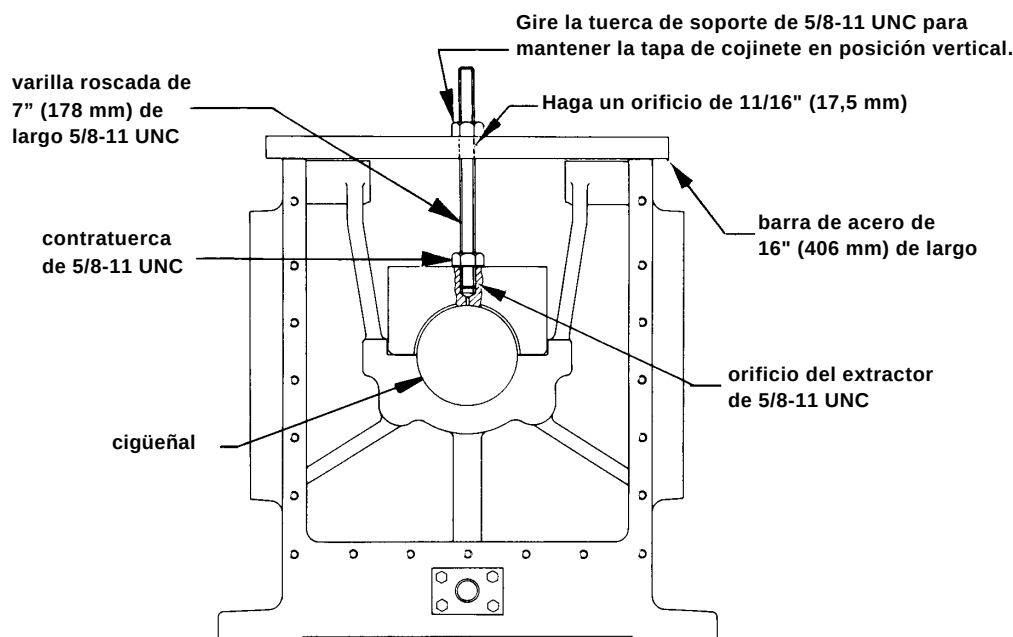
EXTRACTOR DE TAPAS DE COJINETES
